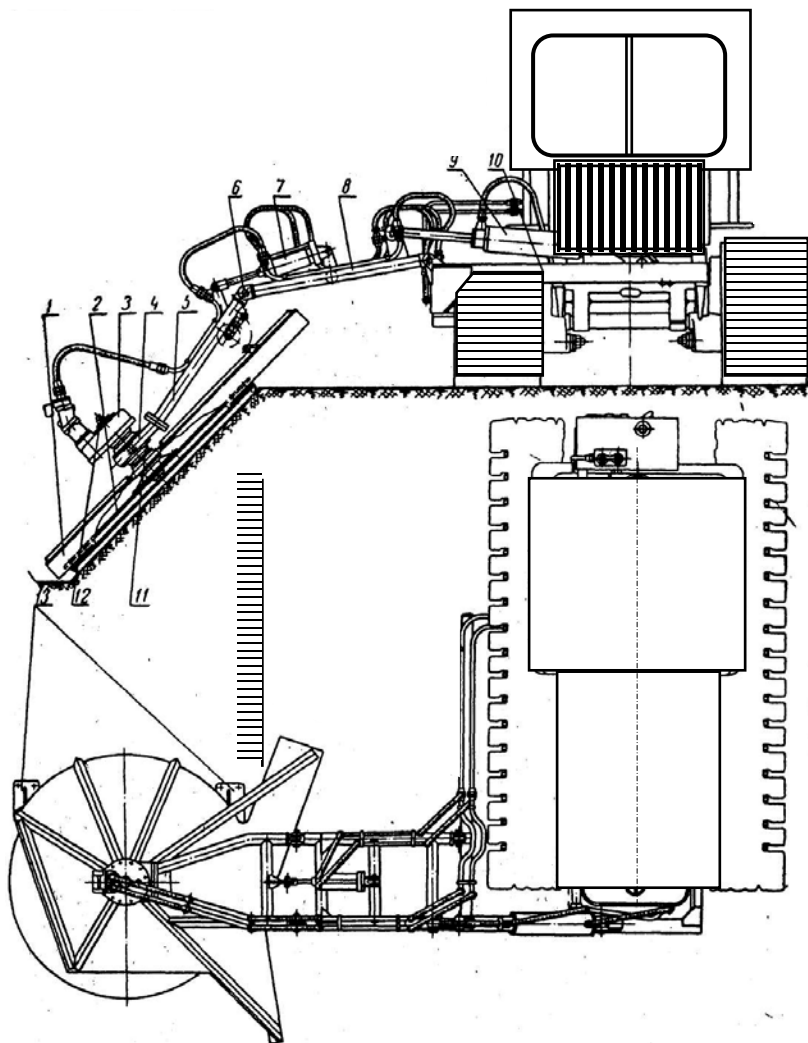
Общее устройство однороторной полунавесной косилки: 1 – кожух; 2 – ротор; 3 – цилиндрический редуктор; 4 – шаровый шарнир; 5 – рукоять; 6 – пальцы; 7, 9 – гидроцилиндры; 8 – рама рабочего органа; 10 – основная рама; 11 – вал; 12 – гидромотор; 13 – лыжи
